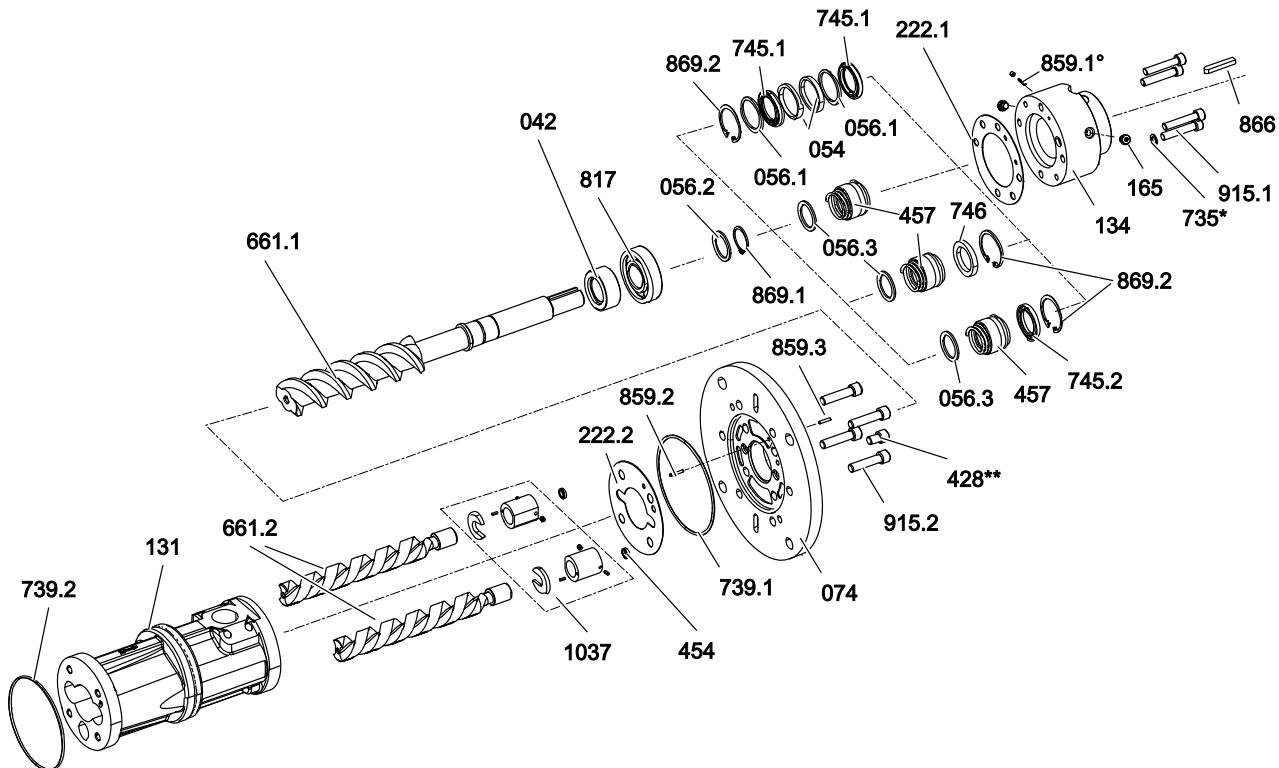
Pièces de rechange CLE 15 – 660, CLE 880
